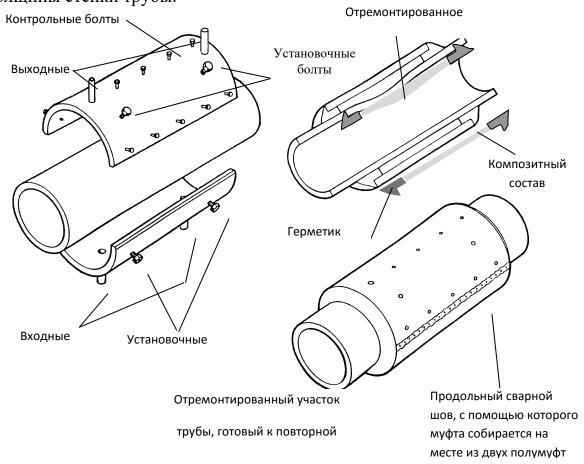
Ремонтная муфта со сварным соединением полумуфт
